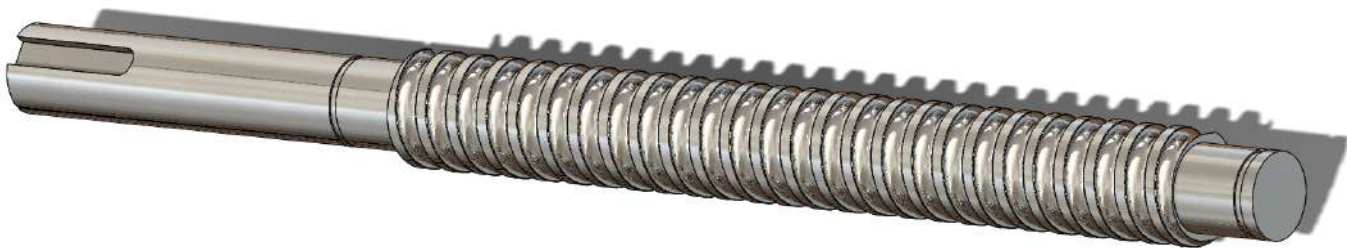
Image 3D illustrant la vis à billes usinée
